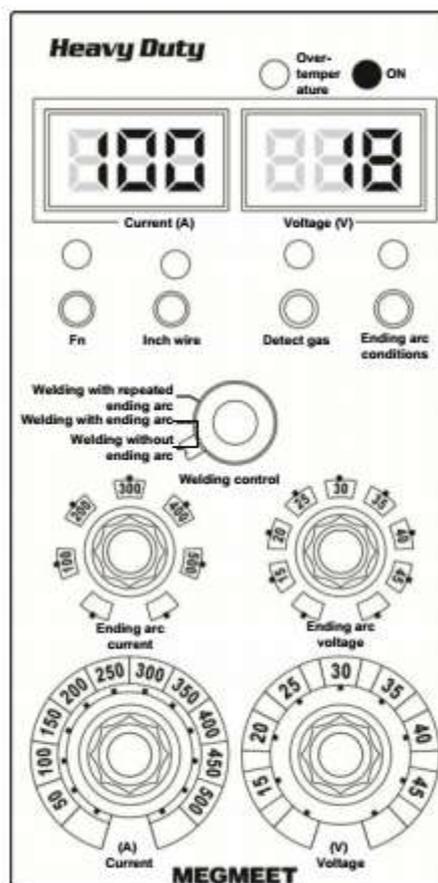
Выбор режима сварки без заварки кратера
